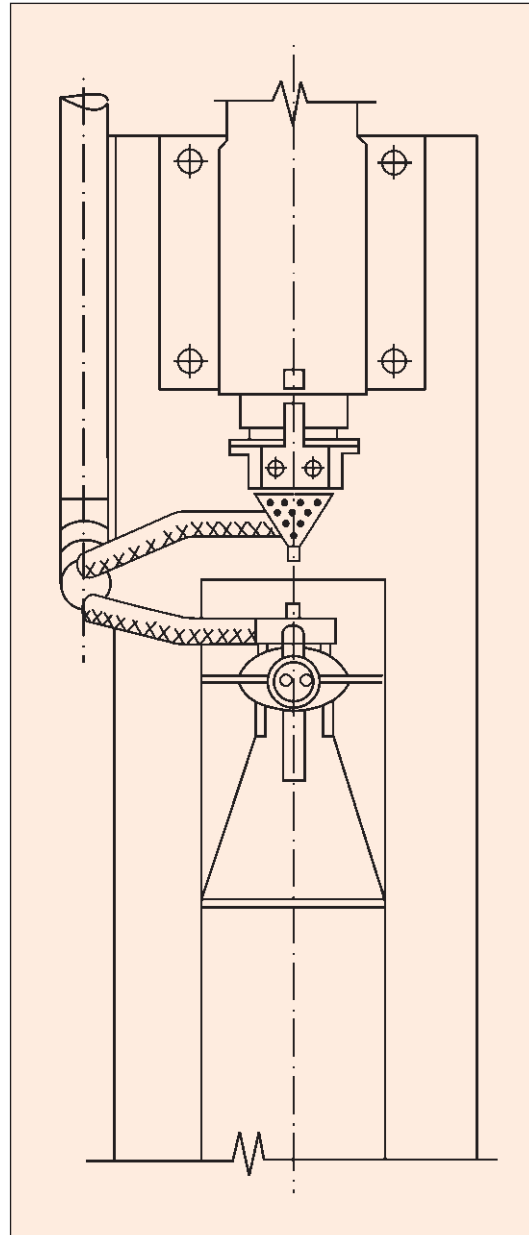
Комбинированный воздухоприемник к машине для контактной сварки
